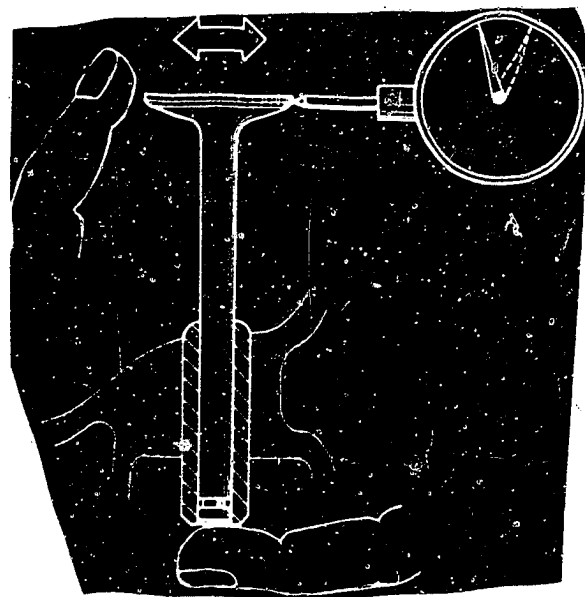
Das Messen des Ventilschaftspiels mit einer Tastuhr.
